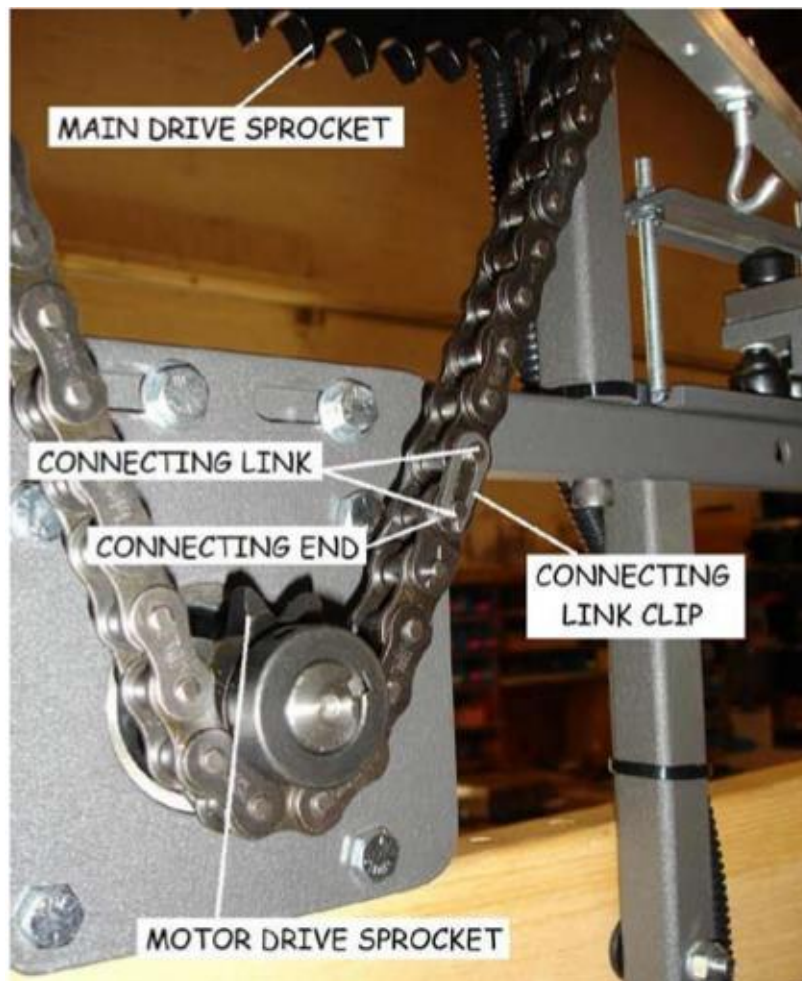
Hauptantriebskettenrad mit Motor und Kette (Innenansicht)
